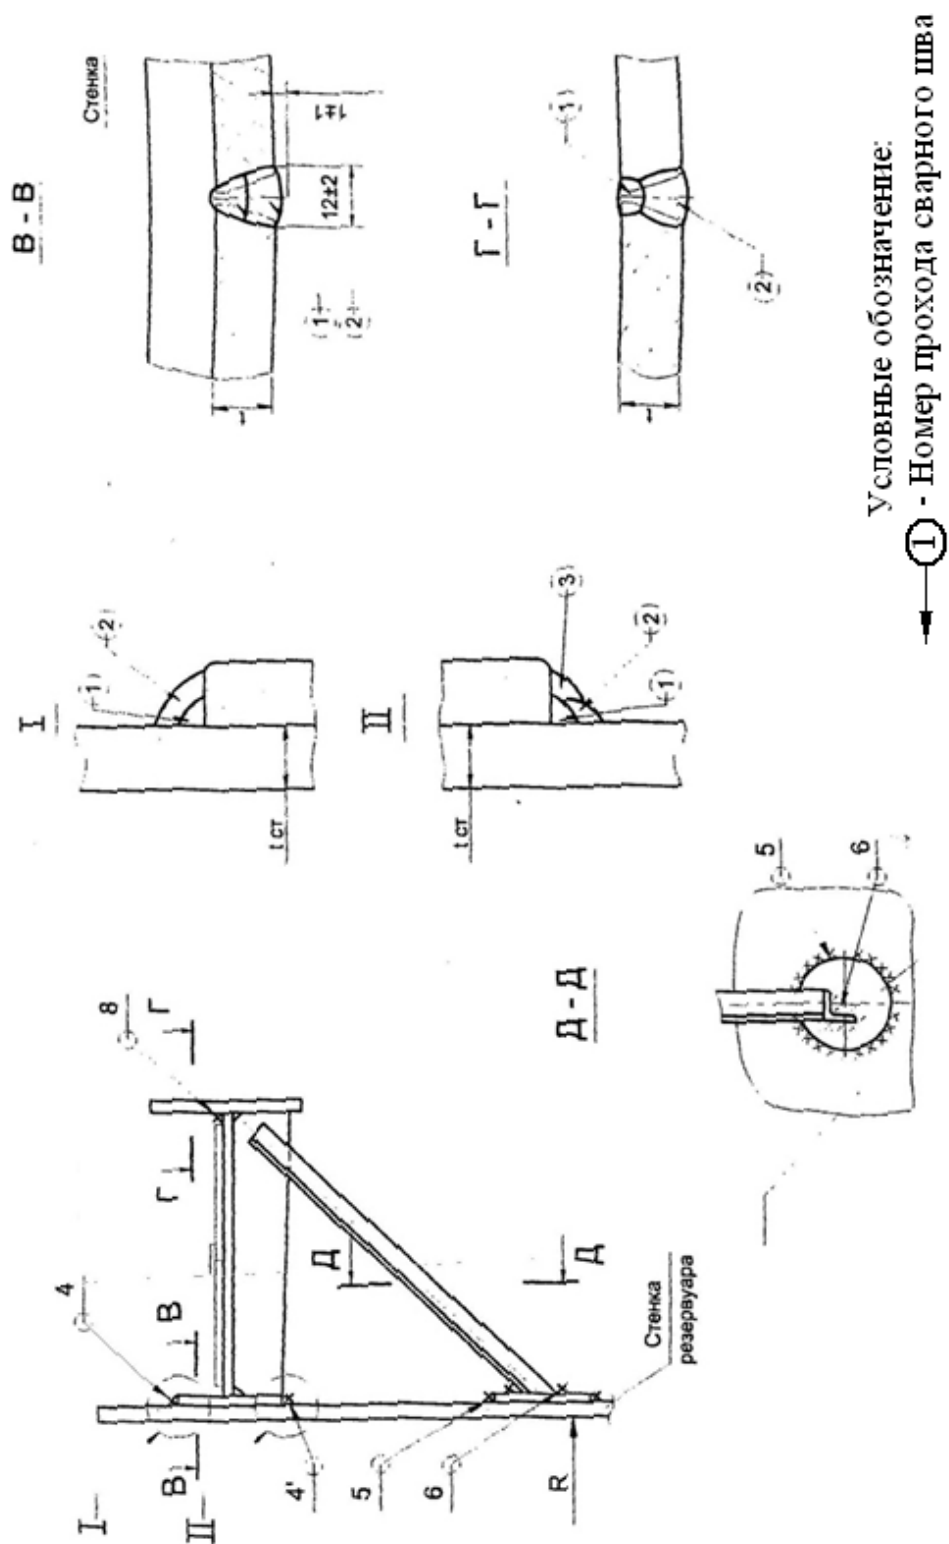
Последовательность и схема сварки швов ветрового кольца
